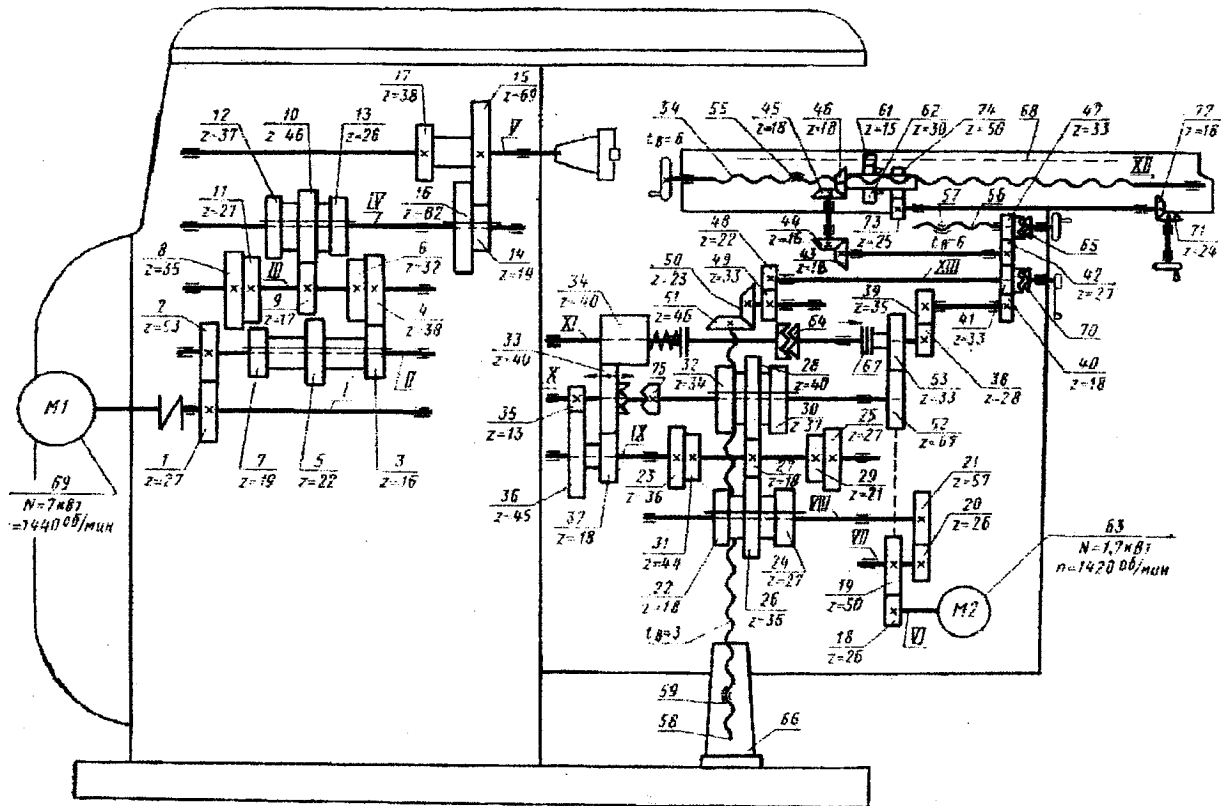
Кінематична схема універсального горизонтально-фрезерного верстата 6М82
